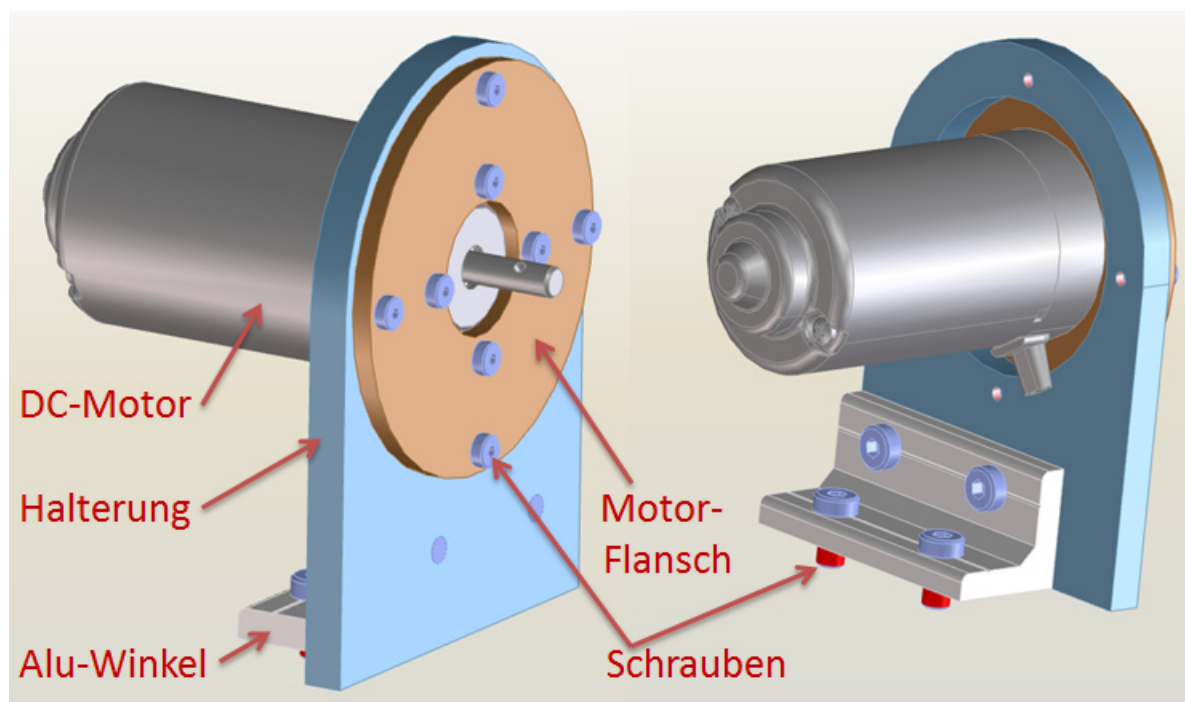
Prüfstand PV1710 CAD-Modell (Detailansicht: Aufnahme für den Prüfling)
